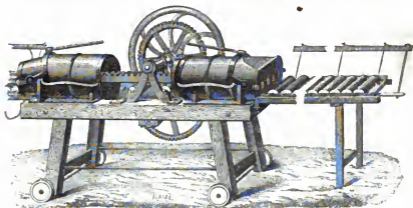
Machine à étirer les tuyaux, système Schlosser.
